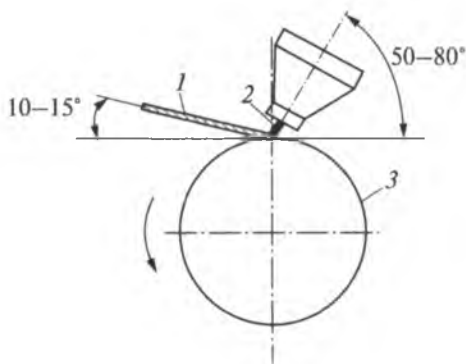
Положение горелки и присадочной проволоки при сварке стыкового соединения:
